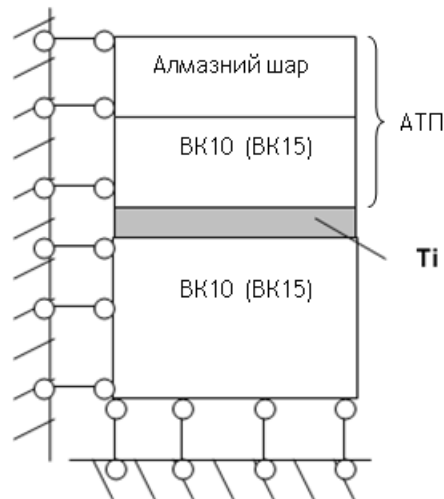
Розрахункова схема зварного з'єднання
